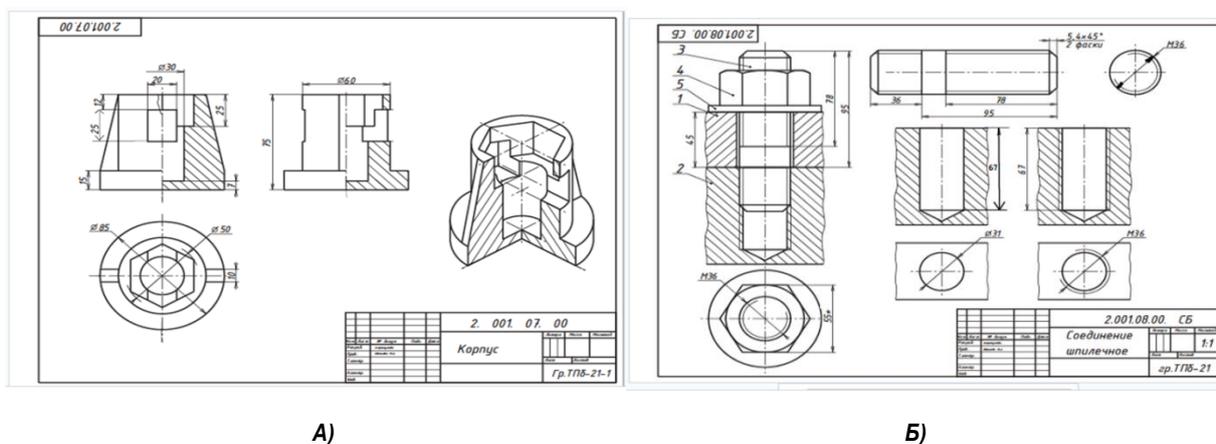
А). Чертеж корпуса. Б). Сборочный чертеж
